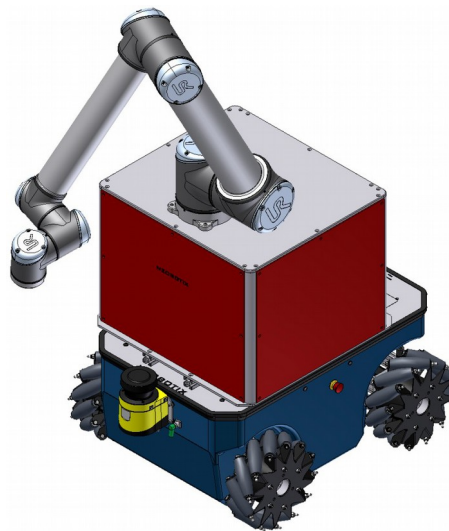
Aluminiumgehäuse und Roboterarm auf der mobilen Plattform
